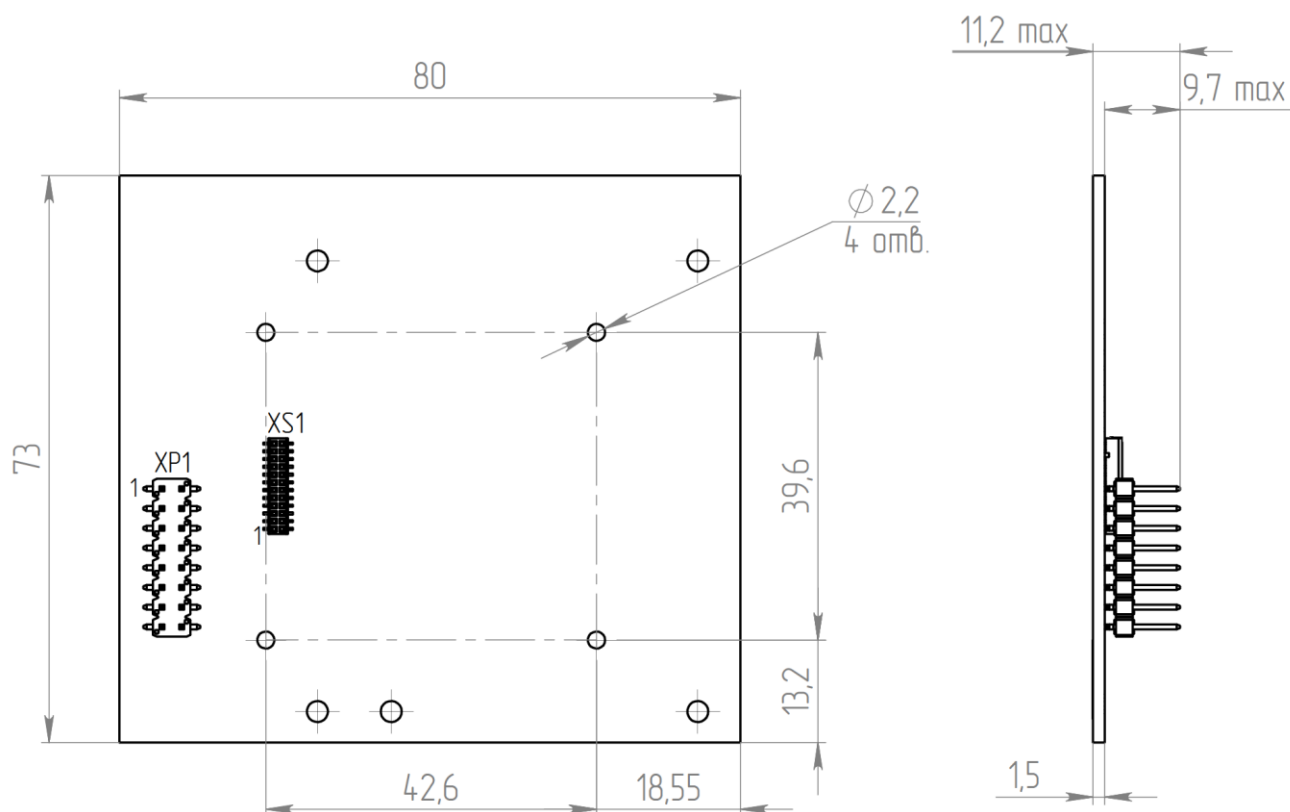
Внешний вид, габаритные размеры изделия, расположение отверстий для крепления
